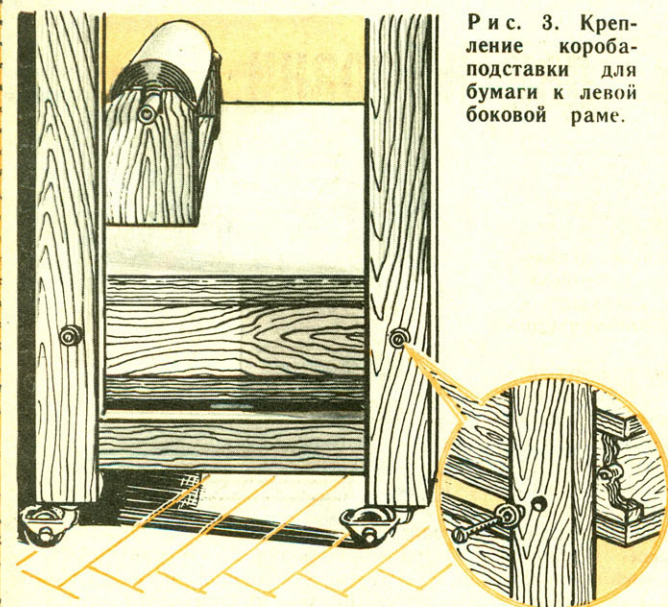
Крепление короба-подставки для бумаги к левой боковой раме.
